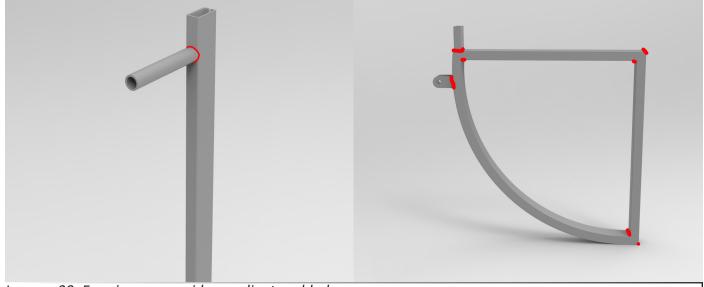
En rojo, zonas unidas mediante soldadura.
